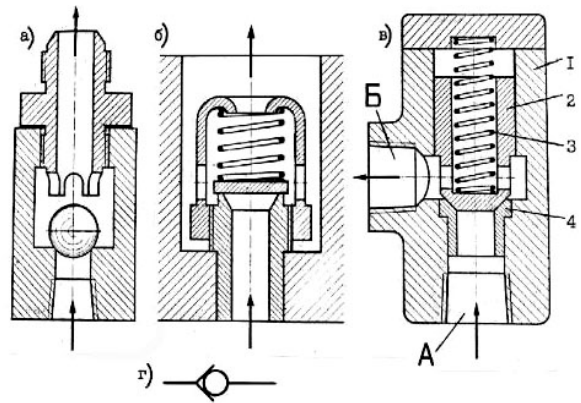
Обратные гидроклапаны: а - шариковый; б - пластинчатый;
